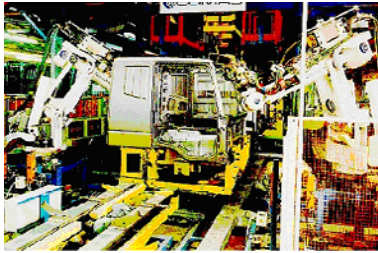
ueZ) Schweißroboter für den Karosseriebau
